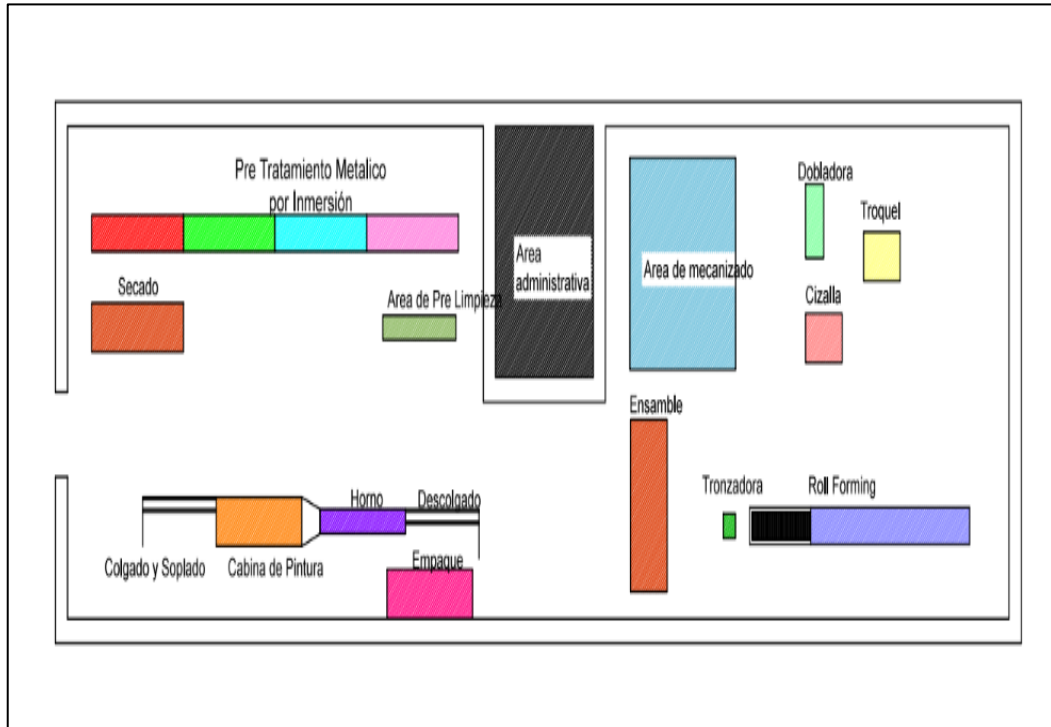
Layout propuesto a la empresa Rubik Assembly C.A.
